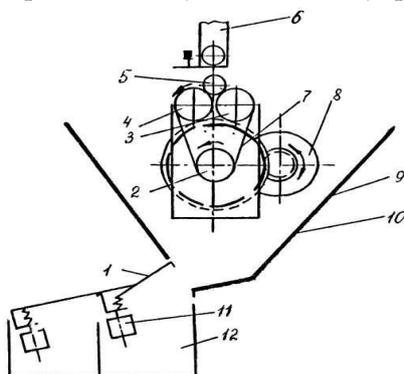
Конструктивная схема устройства: 1 – заслонка сортировочного механизма; 2 – привод вращения валков; 3, 4 – вращающиеся валки; 5 – изделие; 6 – загрузочно-ориентирующее устройство; 7 – ремень привода; 8 – привод рамы; 9 – бункер-ловитель; 10 – покрытие; 11 – электромагнит сортировочного механизма; 12 – кассеты для проконтролированных изделий
